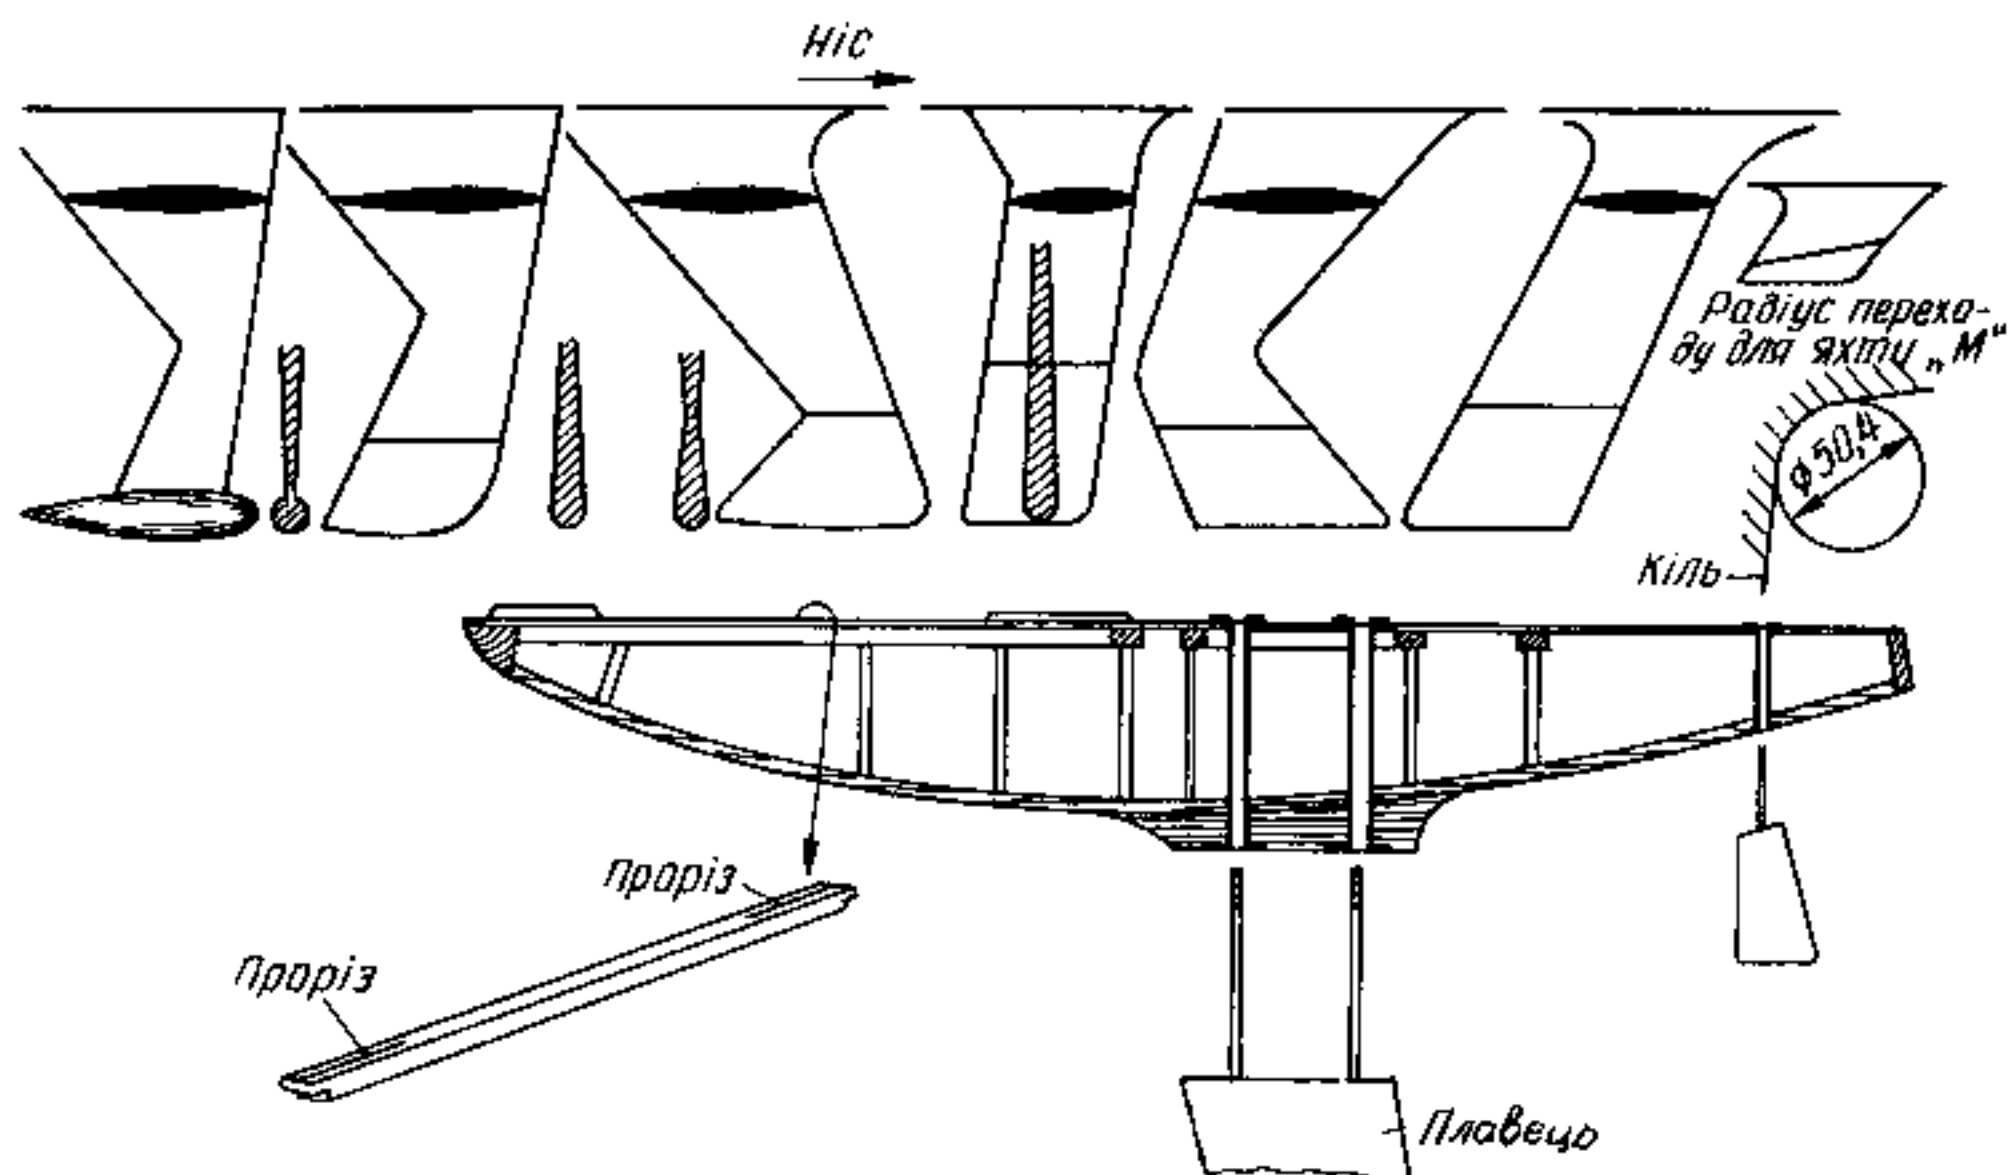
Конструкція корпусу яхти класу «М», форми плавців та прикріплення плавця до корпусу.
